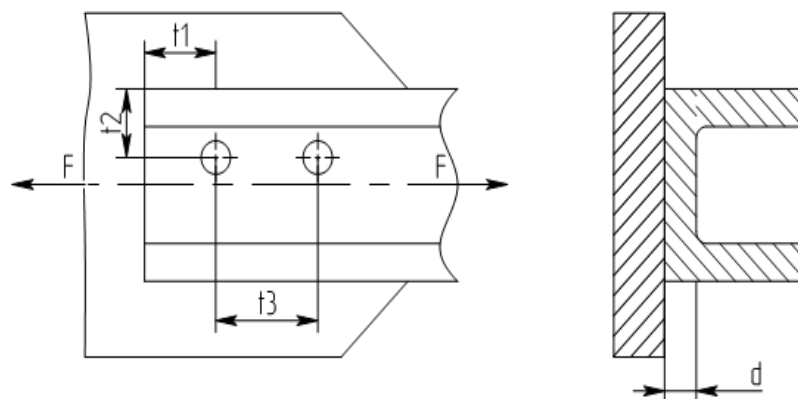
Швеллер, приваренный к косынке точечной сваркой
